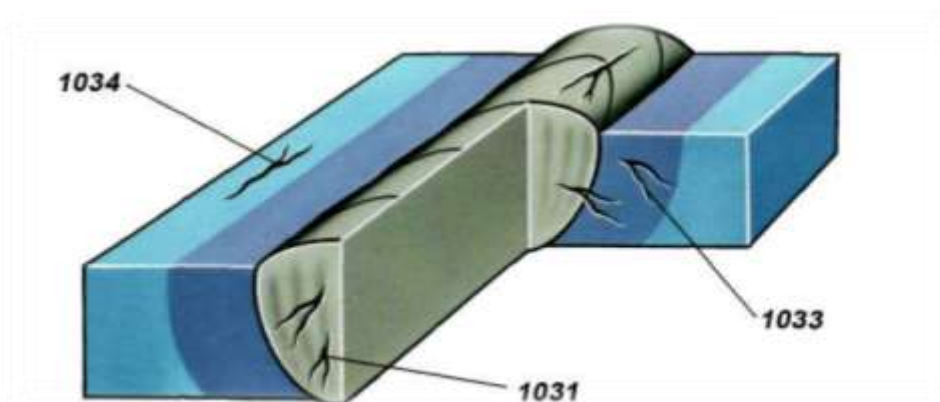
Дефекты сварного шва по типу радиальных трещин
